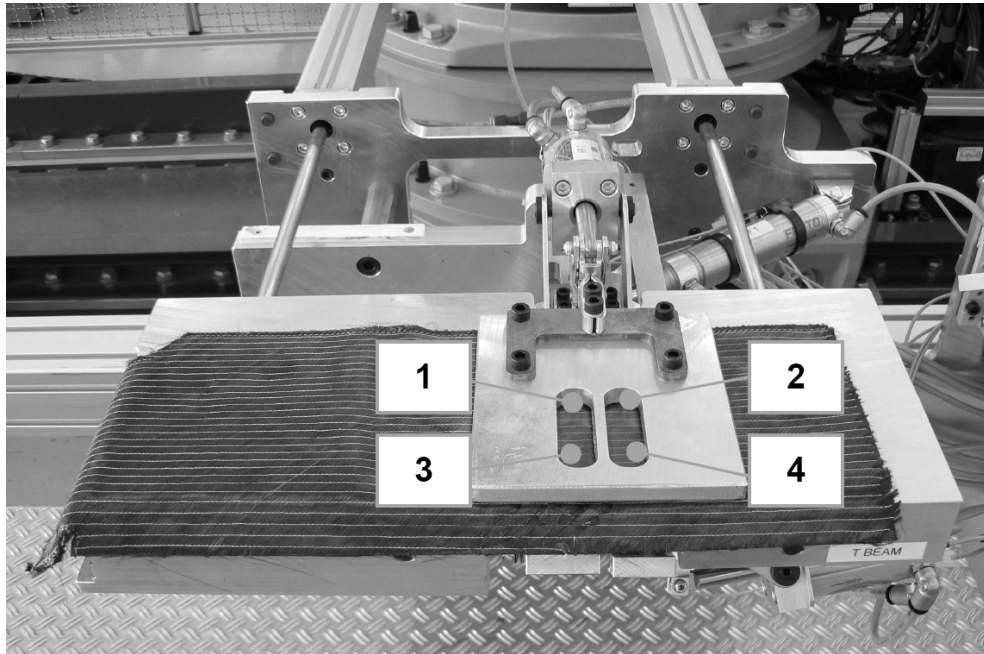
In Preformwerkzeug integrierte Klemmschablone mit Schweißnuten
